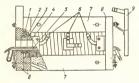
Индуктор для сквозного нагрева цилиндрических мерных заготовок;
